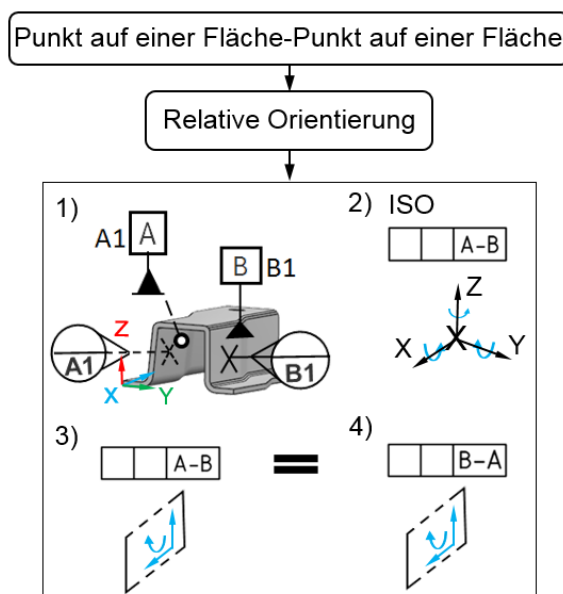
Neue Systematik zum Aufbau: Punkt auf einer Fläche-Punkt auf einer Fläche als gemeinsamer Bezug
